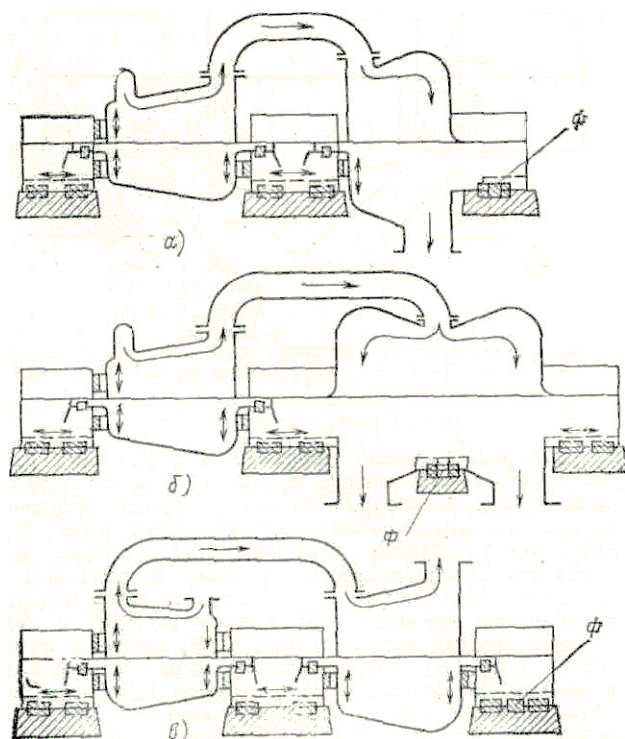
9. Схемы крепления корпусов двухцилиндровых турбин
